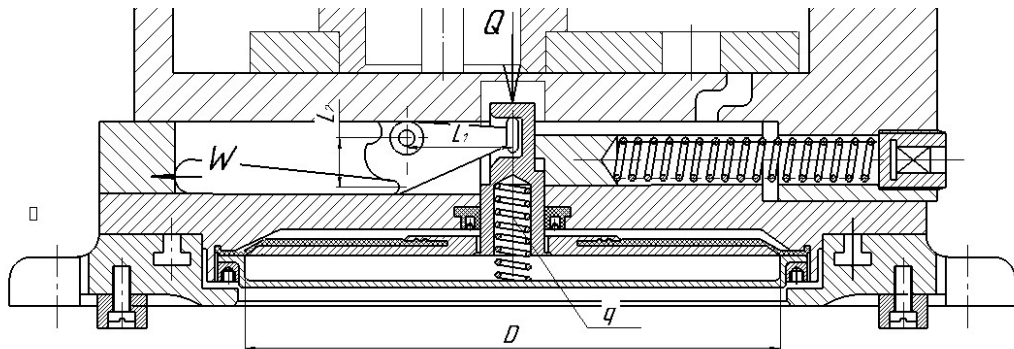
Загальний вигляд приводу пристрою
